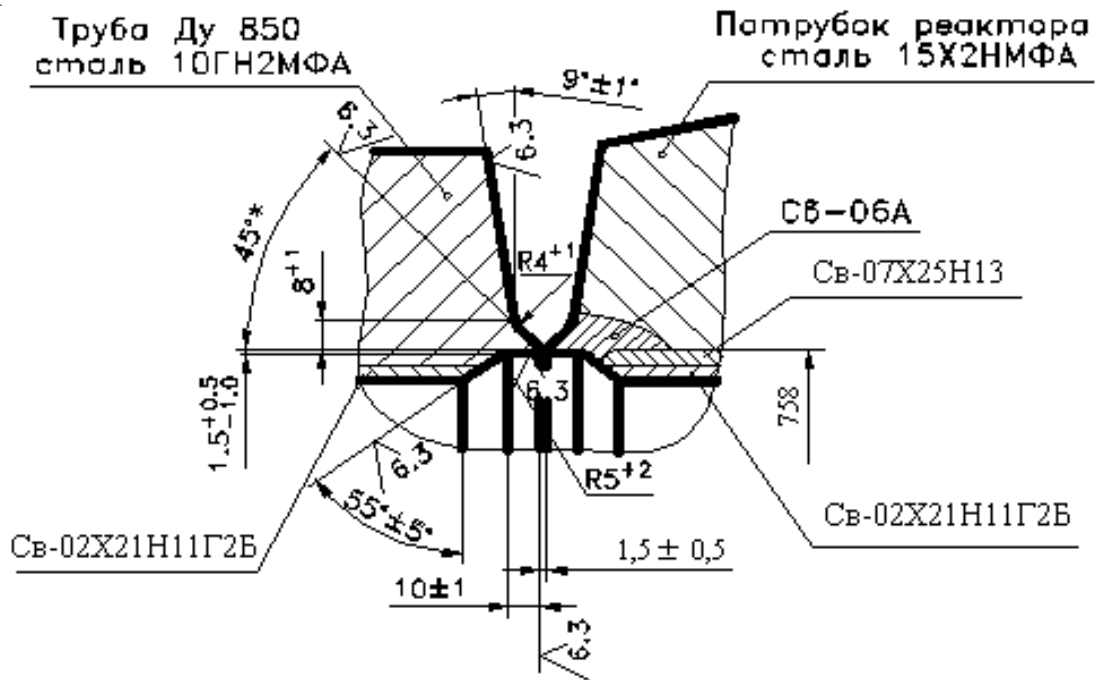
Разделка кромок сварного соединения узла трубного с патрубками корпуса реактора
